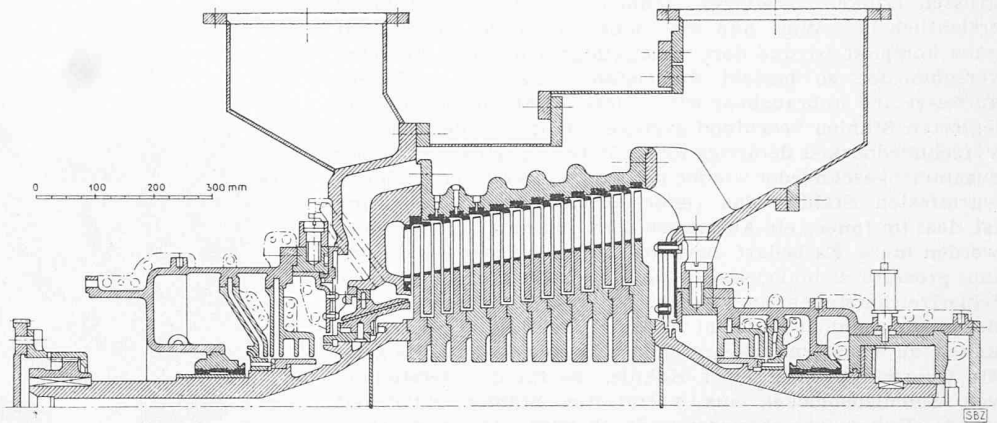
Geschweisste Rotorkonstruktion einer amerikanischen Gasturbine, Masstab 1:12,5 [8]
